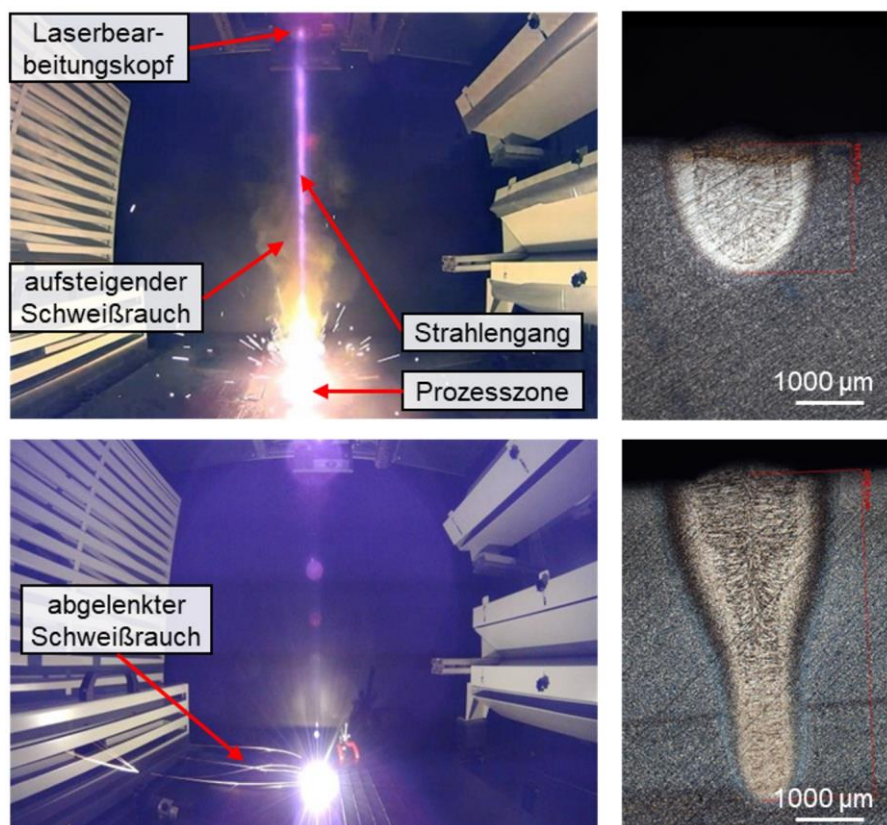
Ausbreitung der Schweißrauche im Bearbeitungsraum (links, oben: ohne zusätzliche Luftströmung, unten: mit mäßiger Luftströmung quer zur Richtung des Laserstrahls) sowie mikroskopische Querschliffbilder der zugehörigen Schweißnähte (rechts). Laserstrahlleistung 3 kW, Fokusbereich ~ 300 µm, Vorschubgeschwindigkeit 2 m/min, Material Baustahl (Hustedt et al. 2016).
